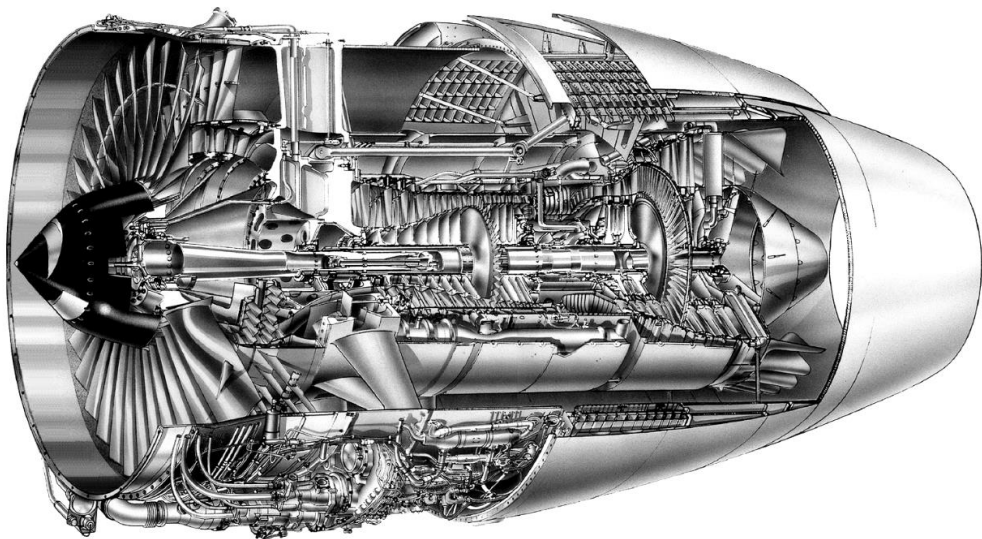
Общий вид турбореактивного двухконтурного двигателя ПС-90А.
